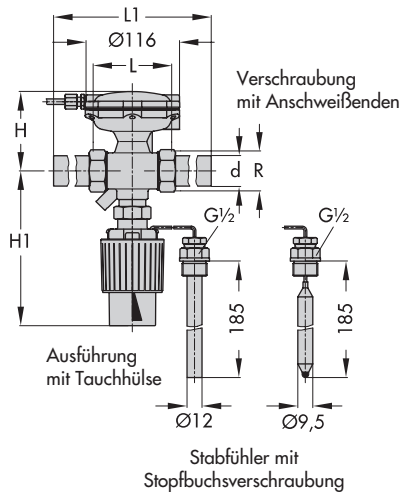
· Maßbilder, Anschraubende, Flansch und Flanschgehäuse
